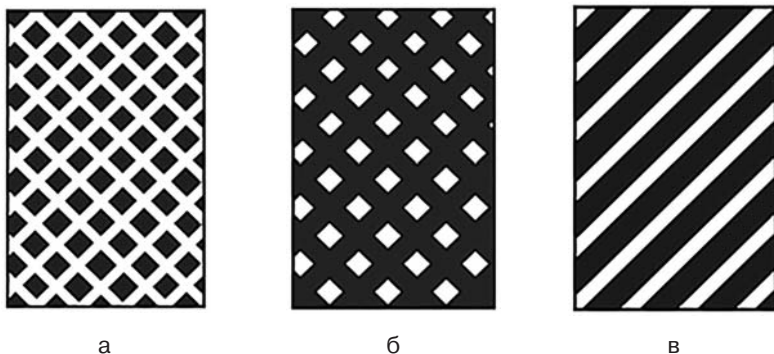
Основні типи розташування різальних елементів (на рис. показані чорним кольором) на робочій поверхні шліфувальної стрічки:
